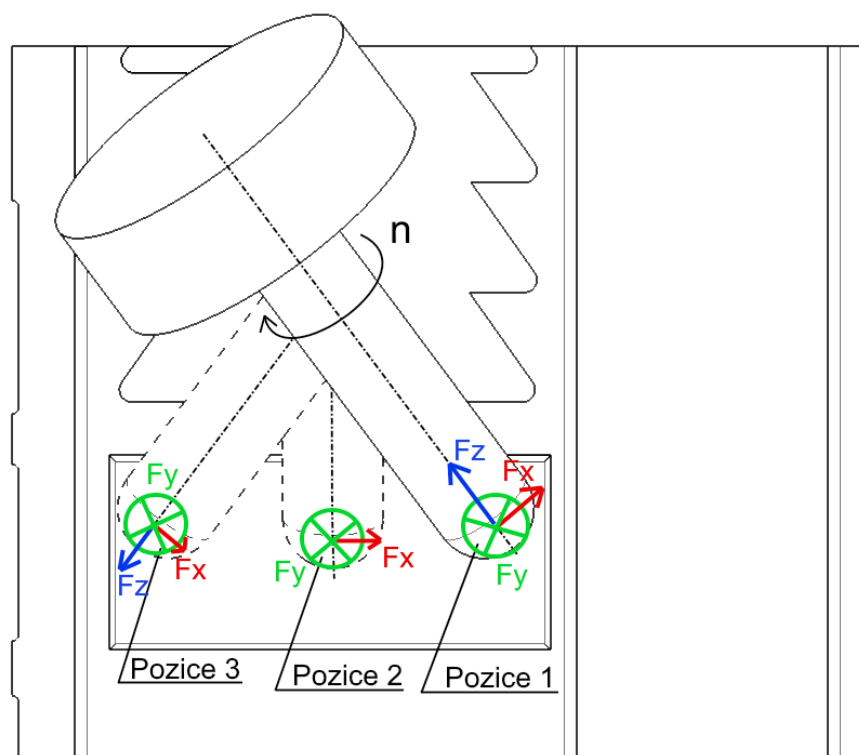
Silový průběh 5-osého pohybu pro soudečkovou frézou s dynamikou stroje.
